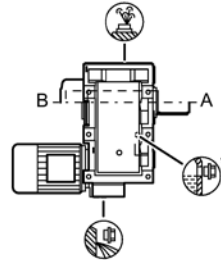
Bauformen für F.28, F. Baugrößen 38B - 188B
